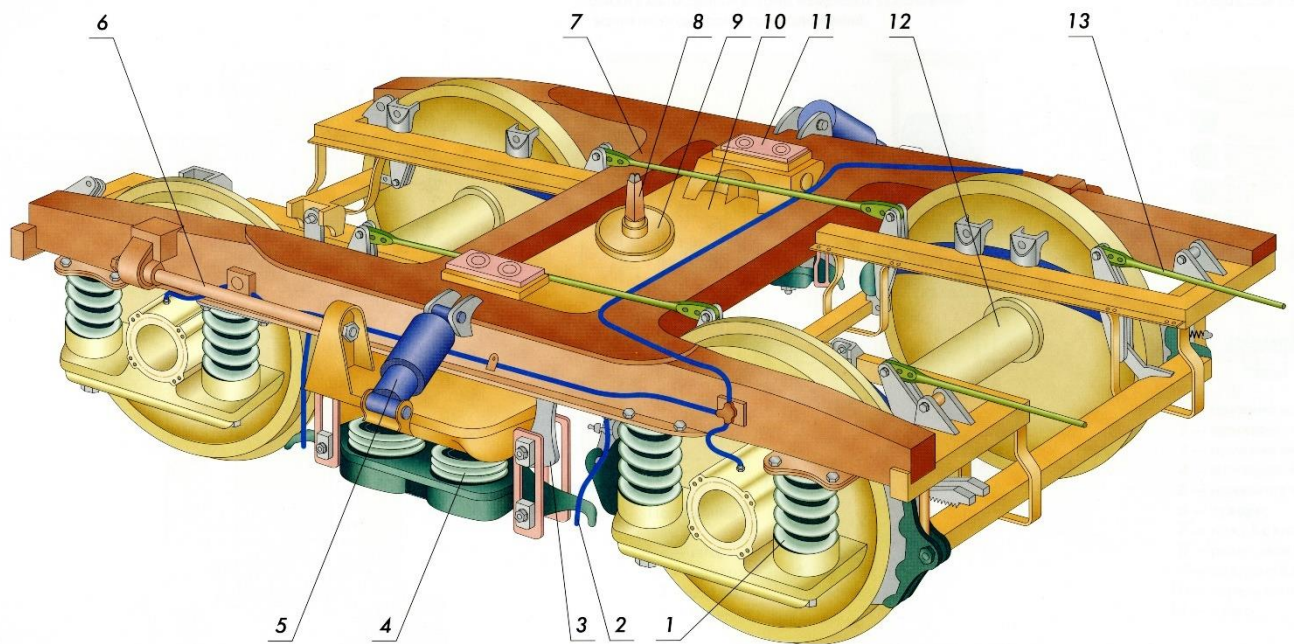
Загальний вигляд візка КВЗ-ЦНП-М
